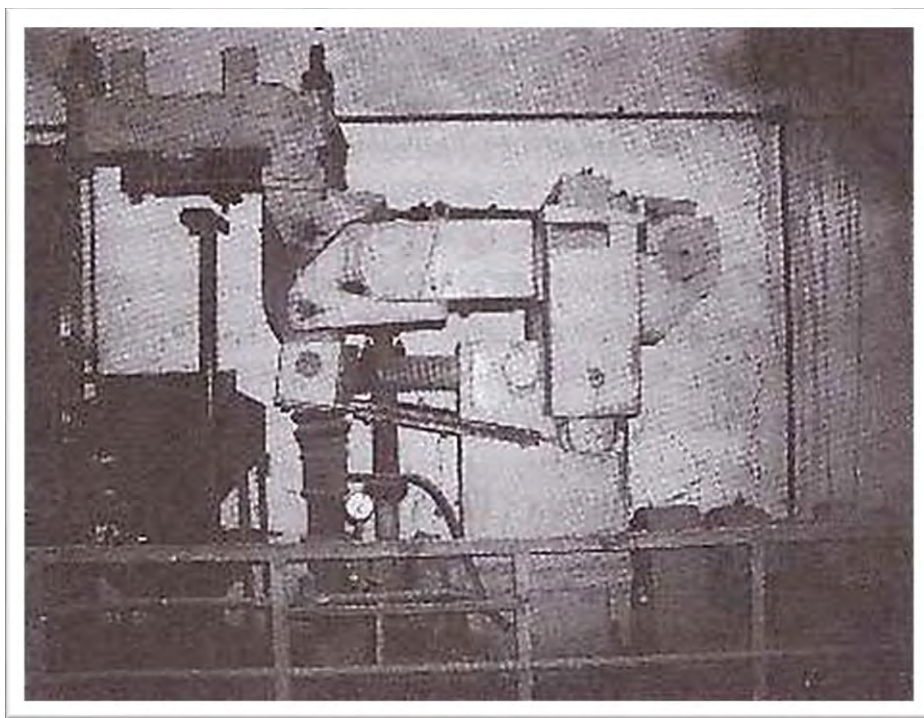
Рессорный механизм качания кристаллизатора конструкции ВНИИМЕТМАШа
